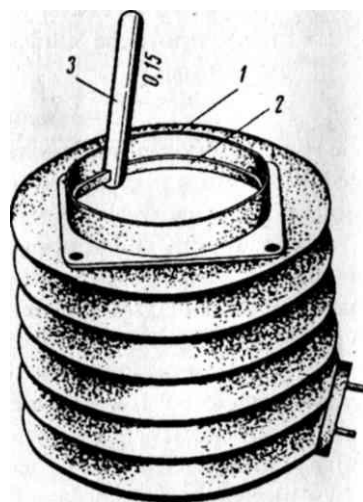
Измерение щупом зазора в замке поршневого кольца: 1 - цилиндр; 2 - поршневое кольцо; 3 - щуп
